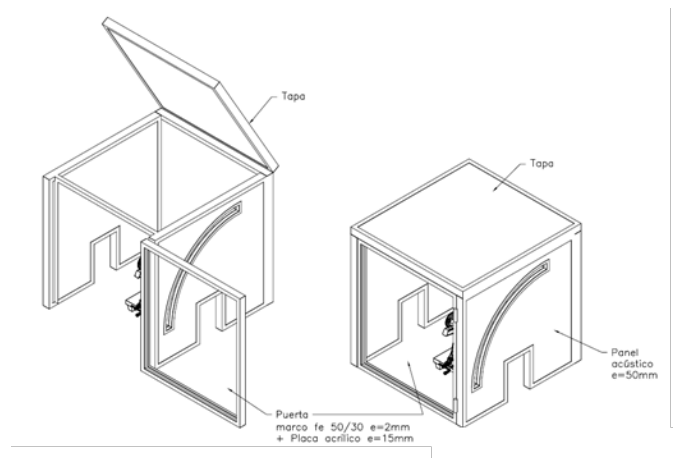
Vistas isométricas de diseño para encierro de tronzadora.
